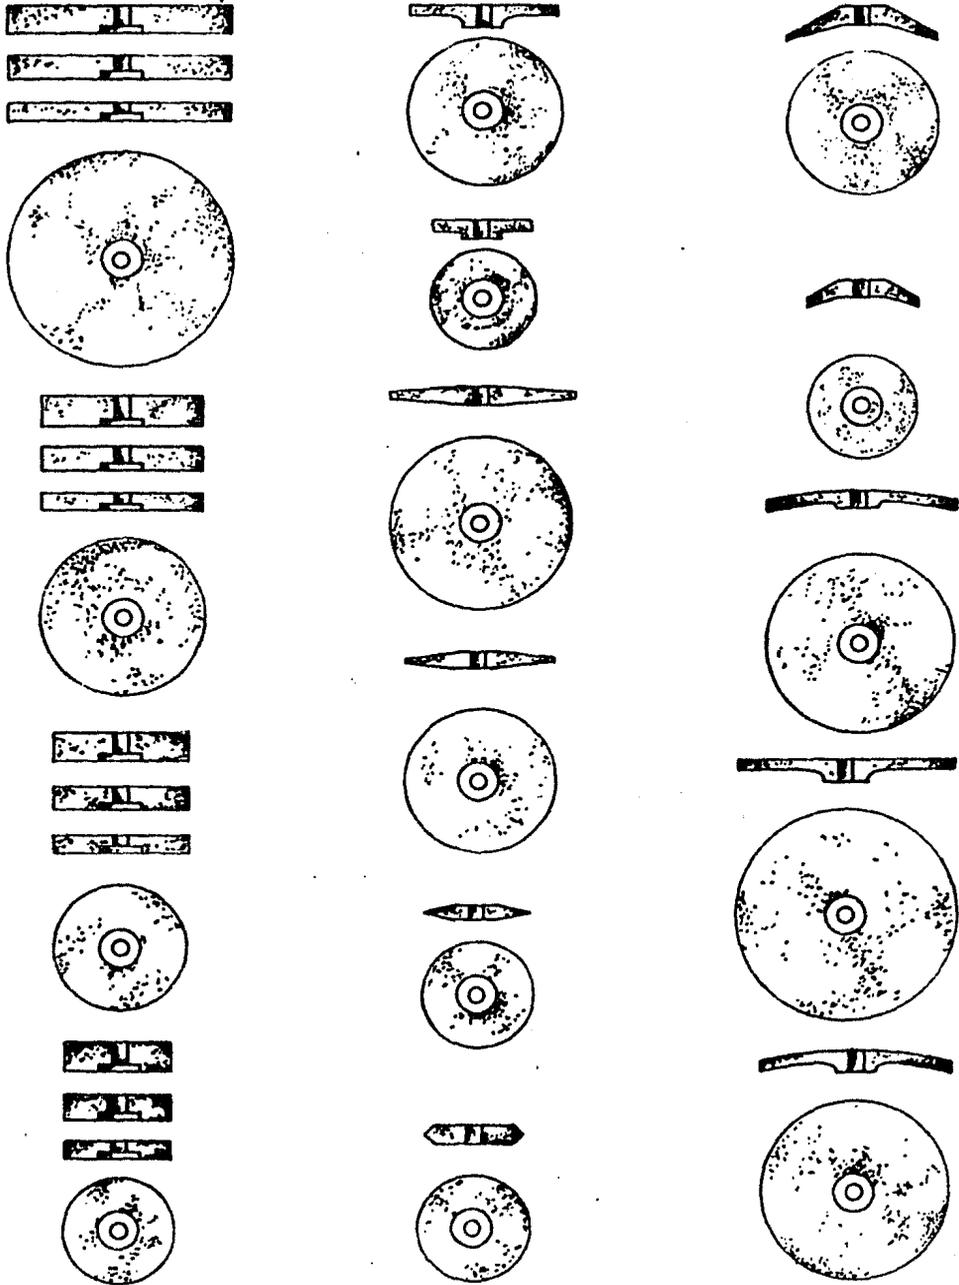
PIEDRAS DE CARBURO PARA MONTAR
